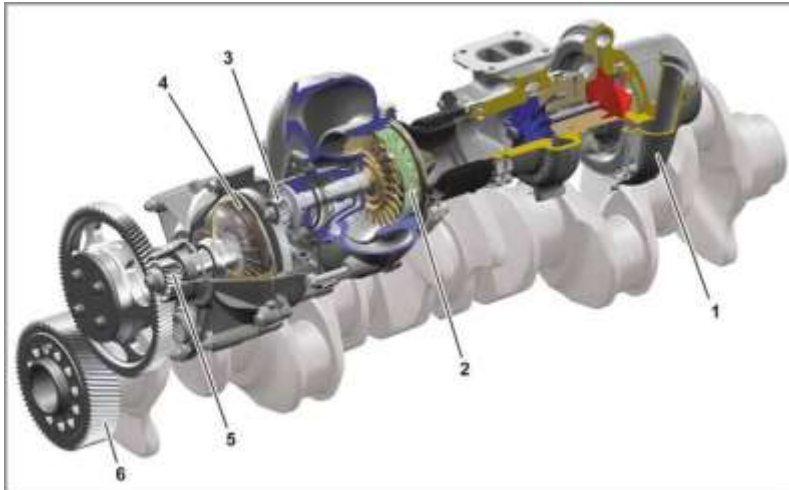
Турбокомпаунд системи наддуву дизеля OM 473: 1 – турбокомпресор; 2 – турбінне колесо; 3 – первинний редуктор; 4 – гідродинамічна муфта; 5 – вторинний редуктор; 6 – колінчастий вал
